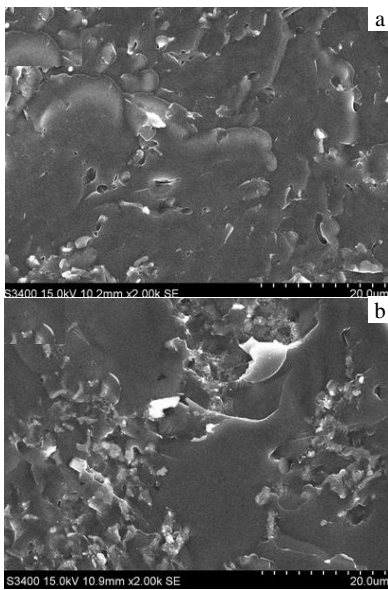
Mg/CuNi/Al 焊接接头断口形貌
